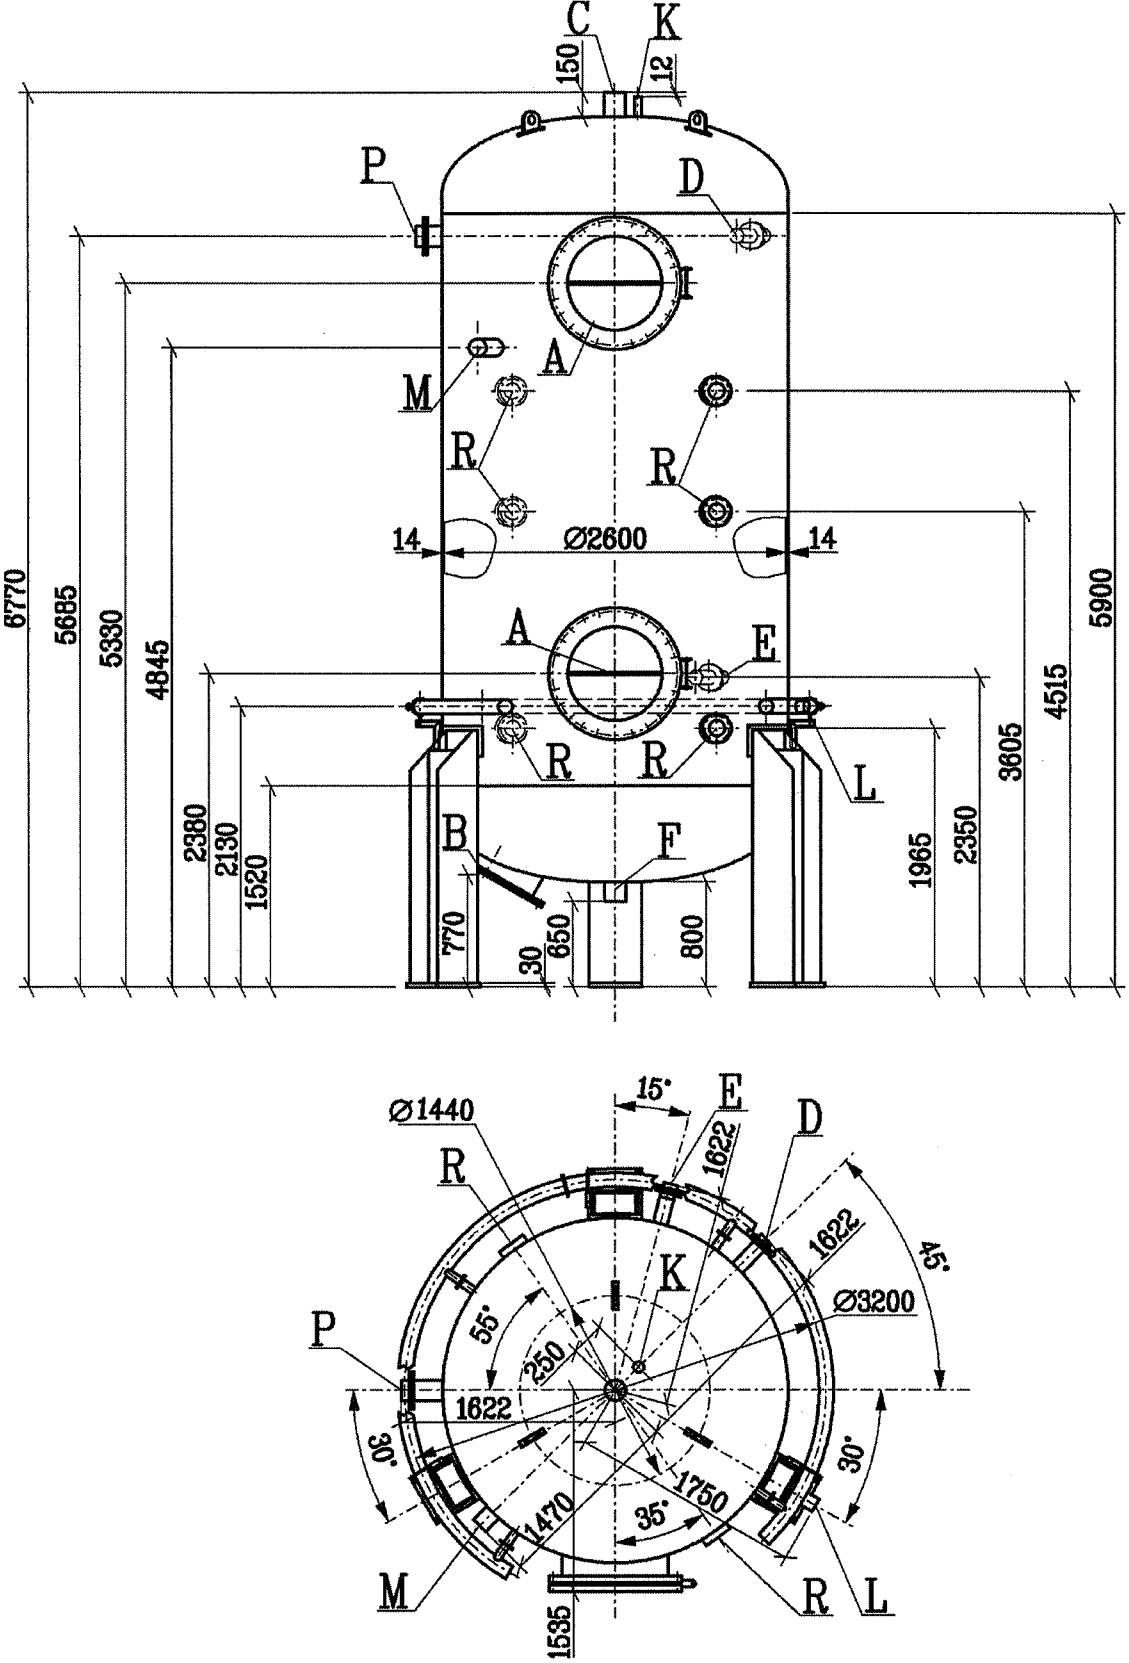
Габаритный чертеж фильтра-регенератора анионита LDP42AT001
